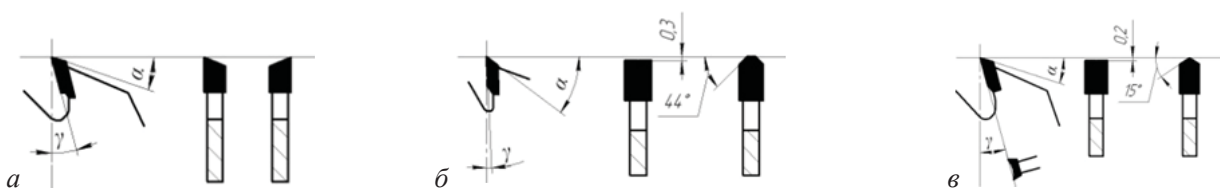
Профили зубьев дисковых пил с пластинами твердого сплава для распиловки ЛДСтП:
